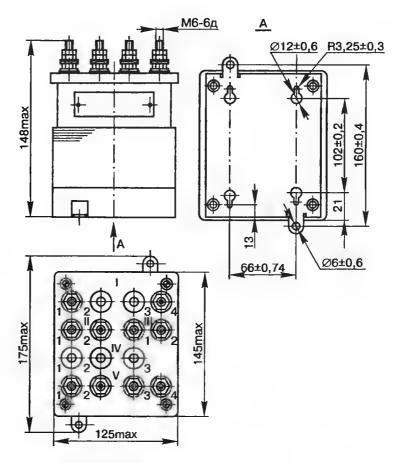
Присоединительные и габаритные размеры трансформатора СОБС-2М
